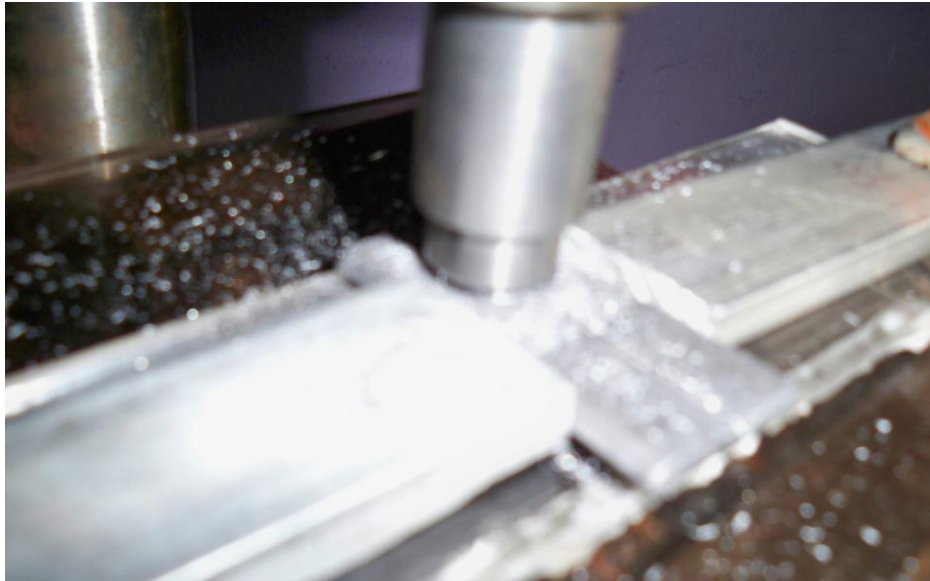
Inicio del proceso de soldadura de las placas
